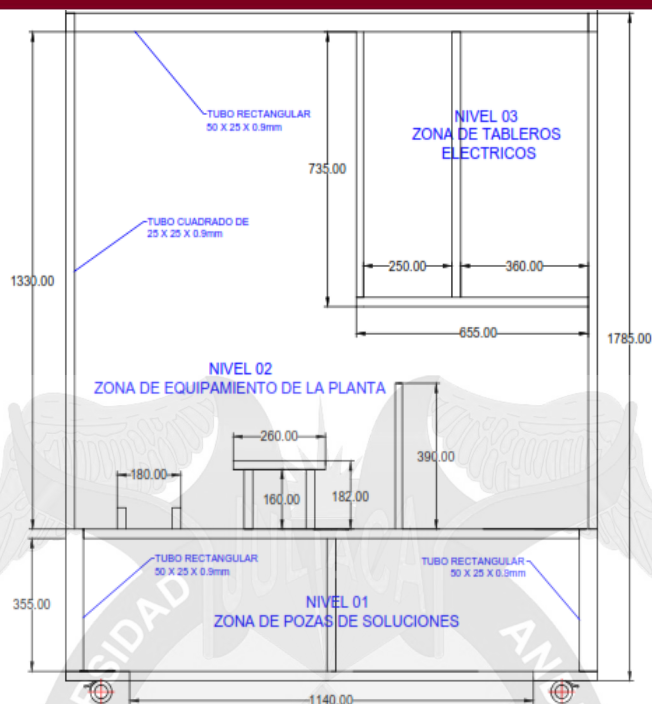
Dimensiones de la estructura metálica de la planta (Vista Frontal)
